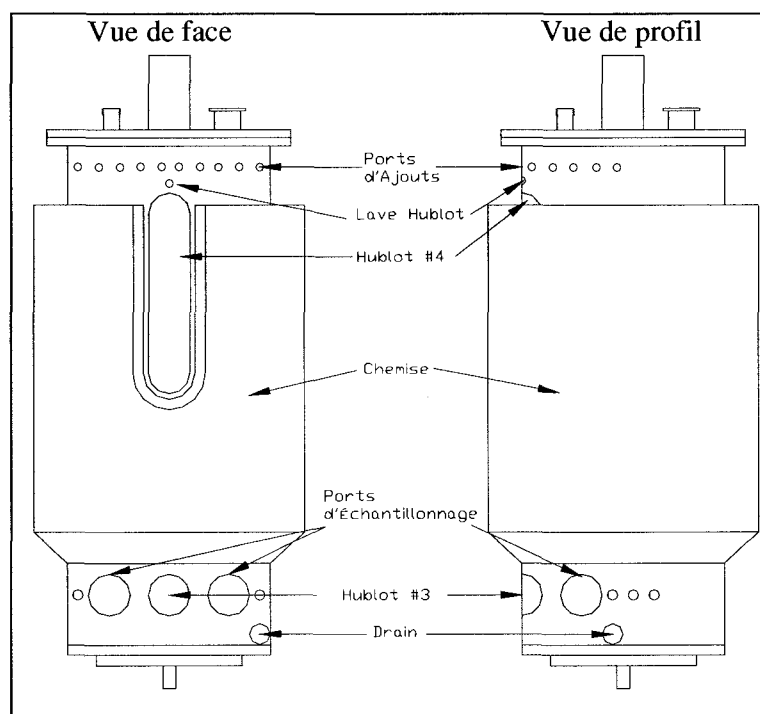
Vue d'ensemble du bioréacteur de 150L
